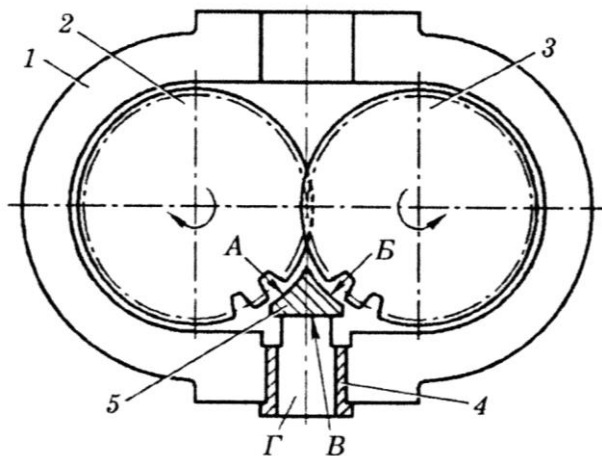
Шестеренний гідромотор з пристроєм для поліпшення його запуску: 1 – корпус; 2 і 3 – шестерні; 4 – втулка; 5 – ущільнювальний конус; А, Б, В – робочі поверхні пристрою, Г – вхідний отвір
